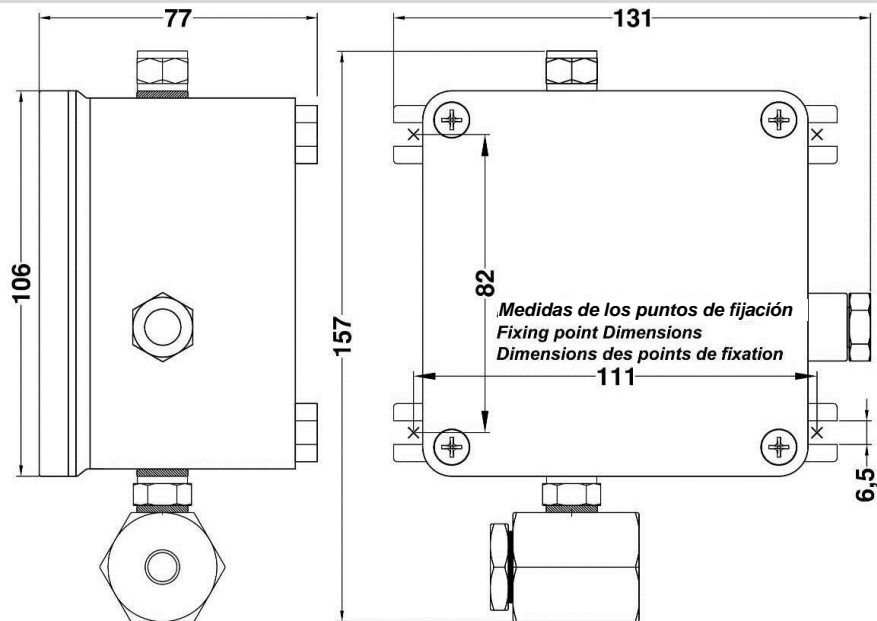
Dimensioni / Dimensiones / Size / Dimensions
